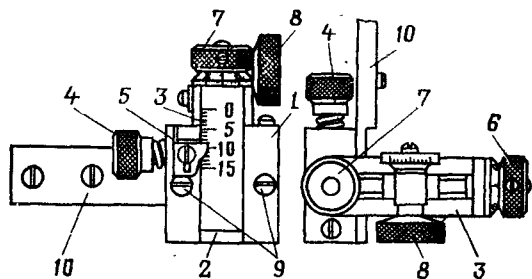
Диоптрический прицел винтовки ТОЗ-8 (вид сбоку и сверху):
